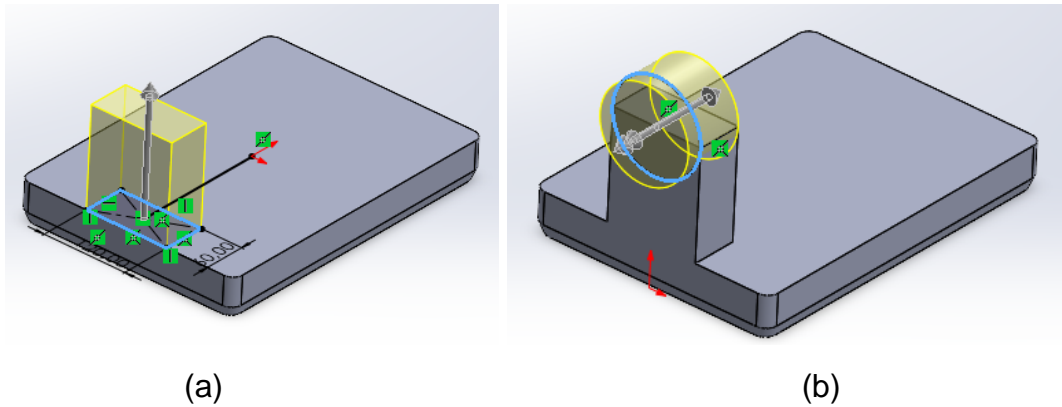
(a) y (b) Extrusión del primer soporte del puente en SolidWorks.
